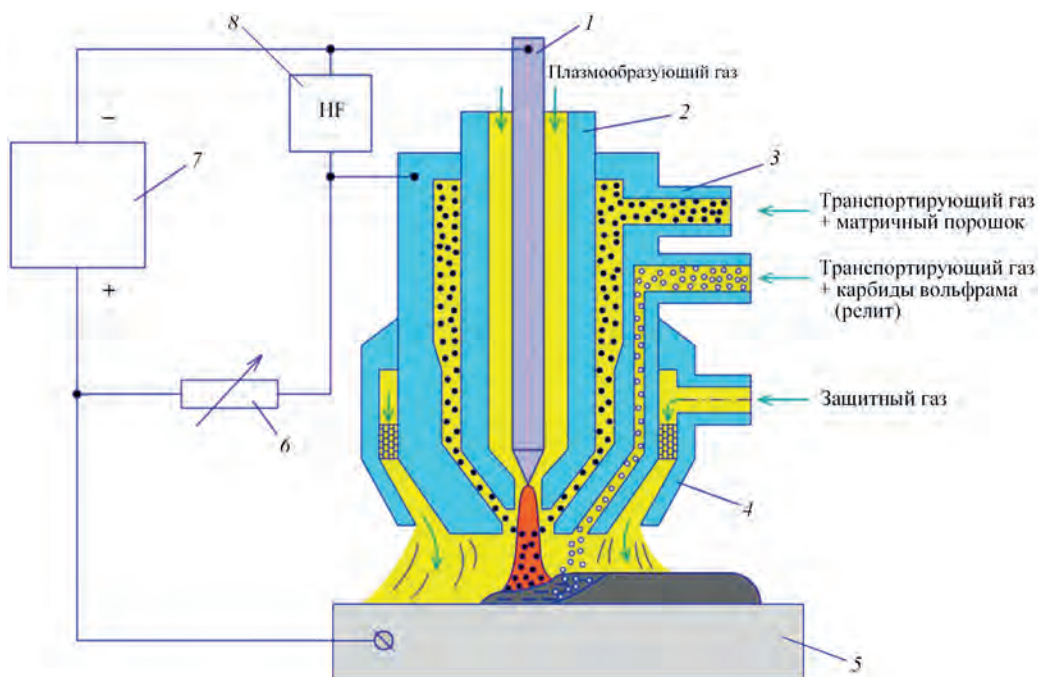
Схема плазменно-порошковой наплавки с подачей релита в хвостовую часть сварочной ванны: 1 – электрод; 2 – сопло плазмообразующее; 3 – сопло фокусирующее; 4 – сопло защитное; 5 – деталь; 6 – балластный реостат; 7 – источник питания; 8 – блок поджига дуги
